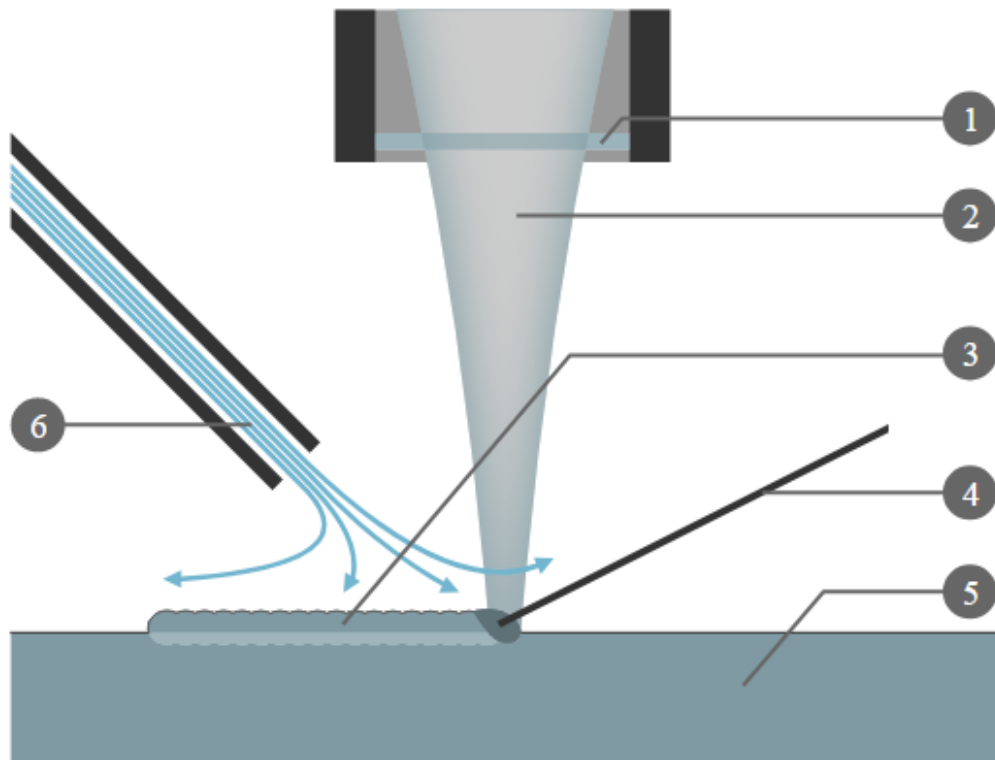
Схема процесу лазерного наплавлення з подачею присадного дроту. 1. Захисне скло об'єктива. 2. Лазерне випромінювання. 3. Наплавлений матеріал. 4. присадний дріт. 5. Деталь. 6. Захисний газ. [4]
